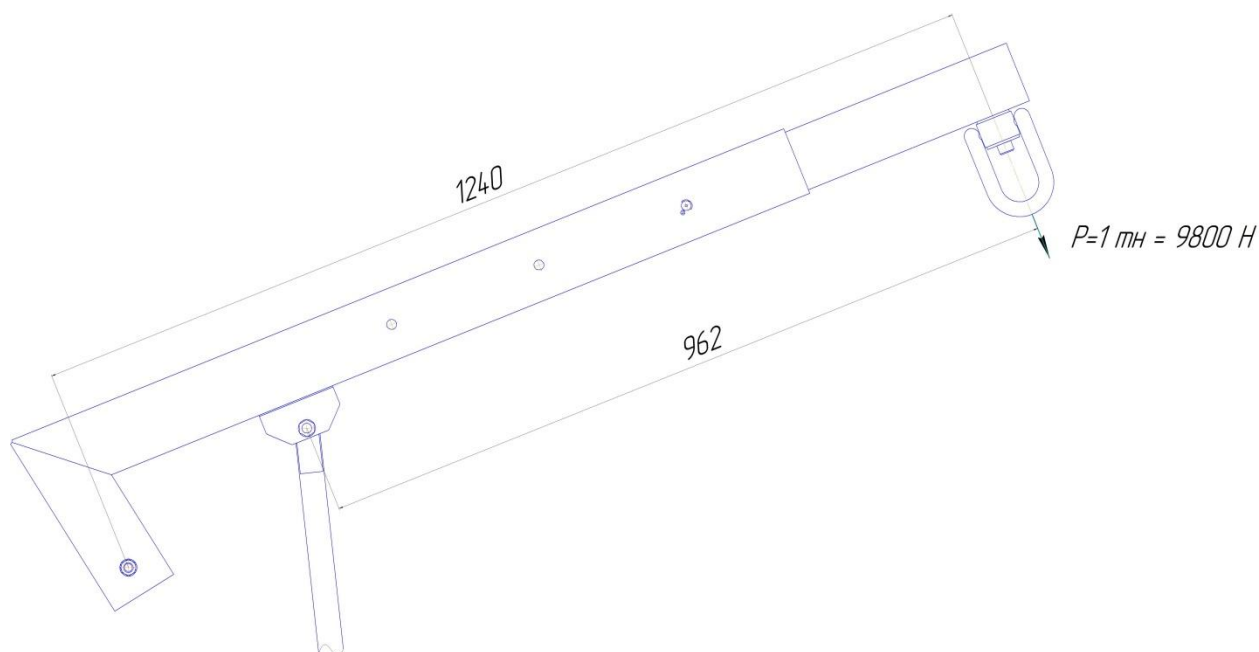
Схема к расчету нагрузки на болт.
